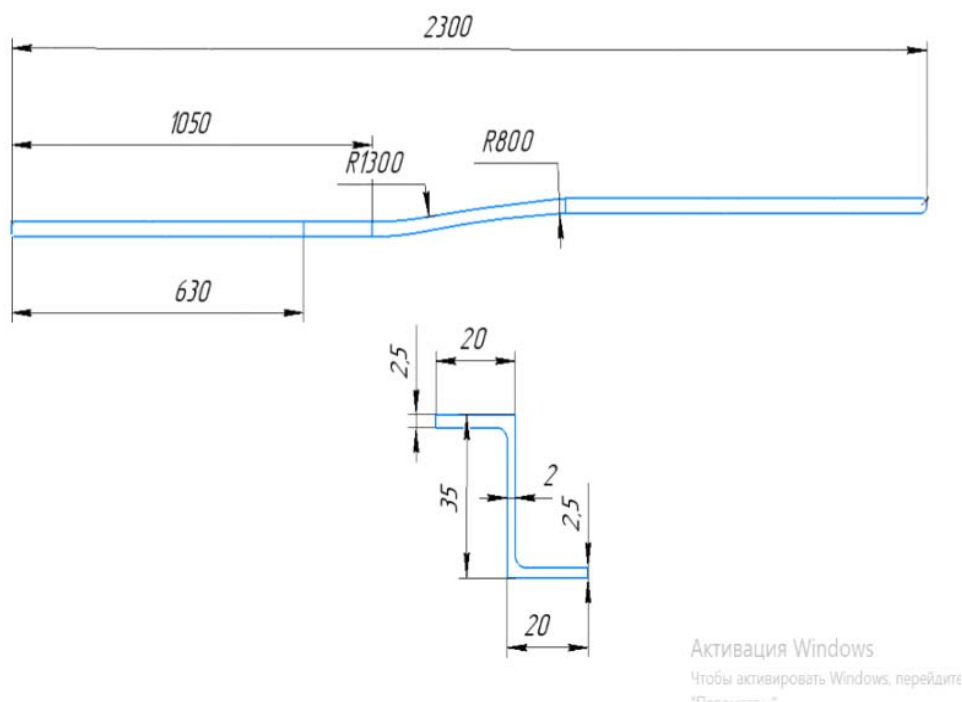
Заготовка стрингера из Z-образного прессованного профиля панели крыла самолета со знакопеременной кривизной.
